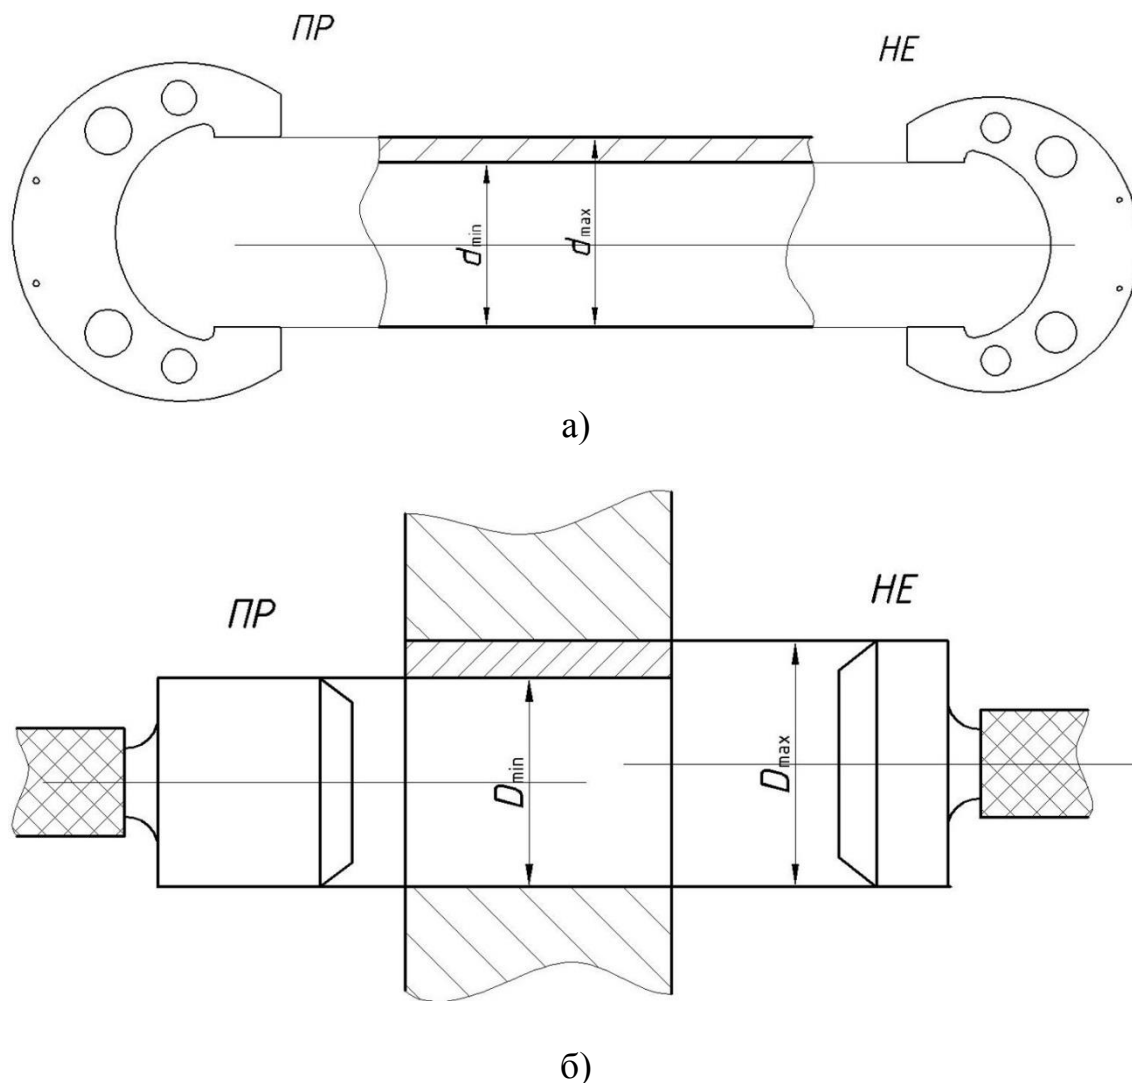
Предельные гладкие калибры: а) калибр-скоба для контроля вала; б) калибр-пробка для контроля отверстия
